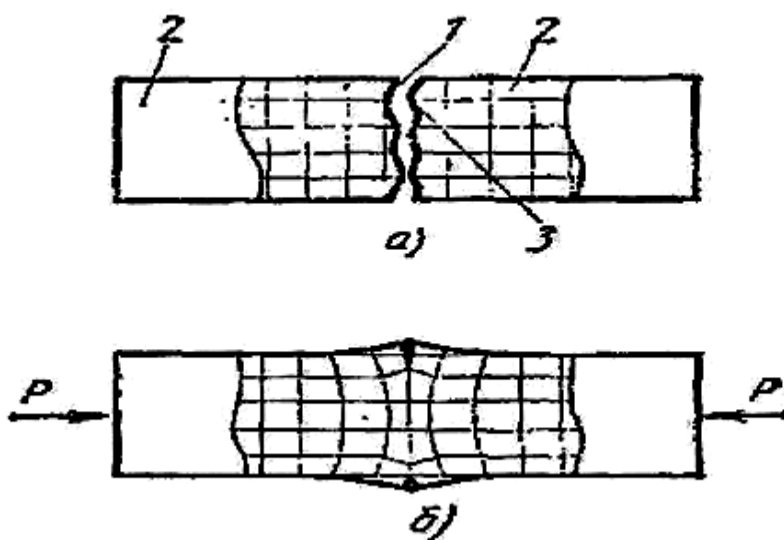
Схема образования сварного соединения в твердом состоянии
